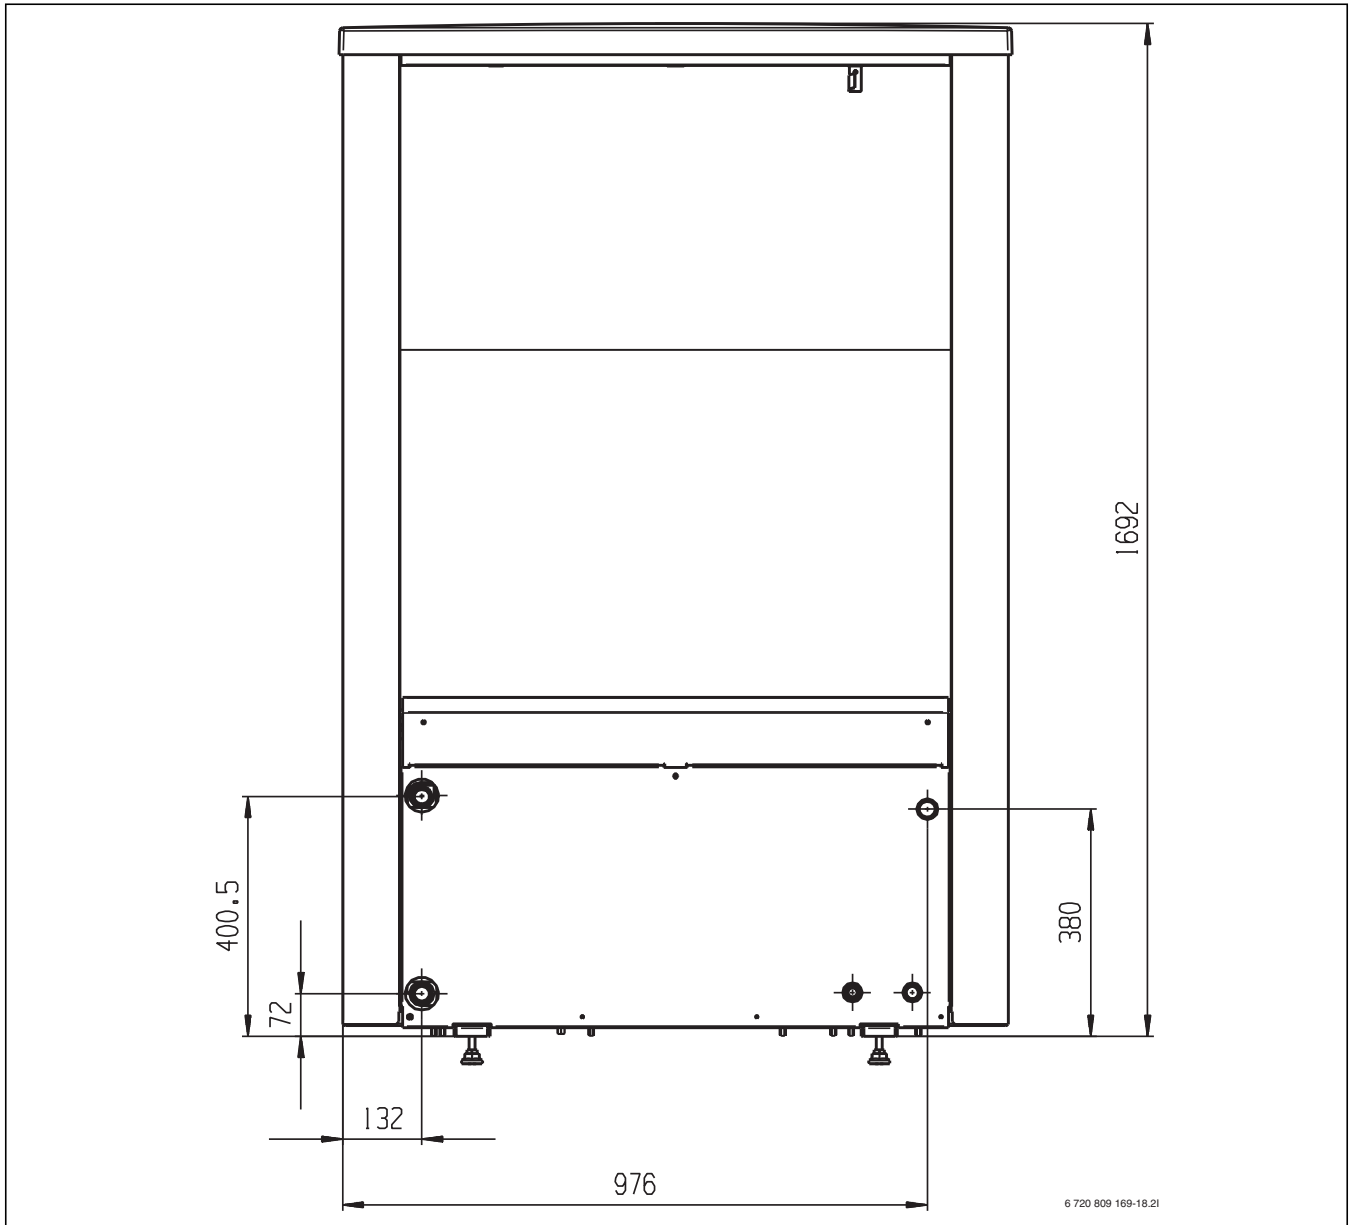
Размеры и присоединения теплового насоса, тыльная сторона, типоразмеры 13-17
